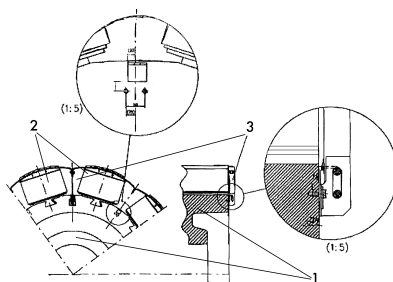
Усовершенствованная конструкция крепления демпферной обмотки: 1 — ступица ротора; 2 — полюс ротора; 3 — шпилька
